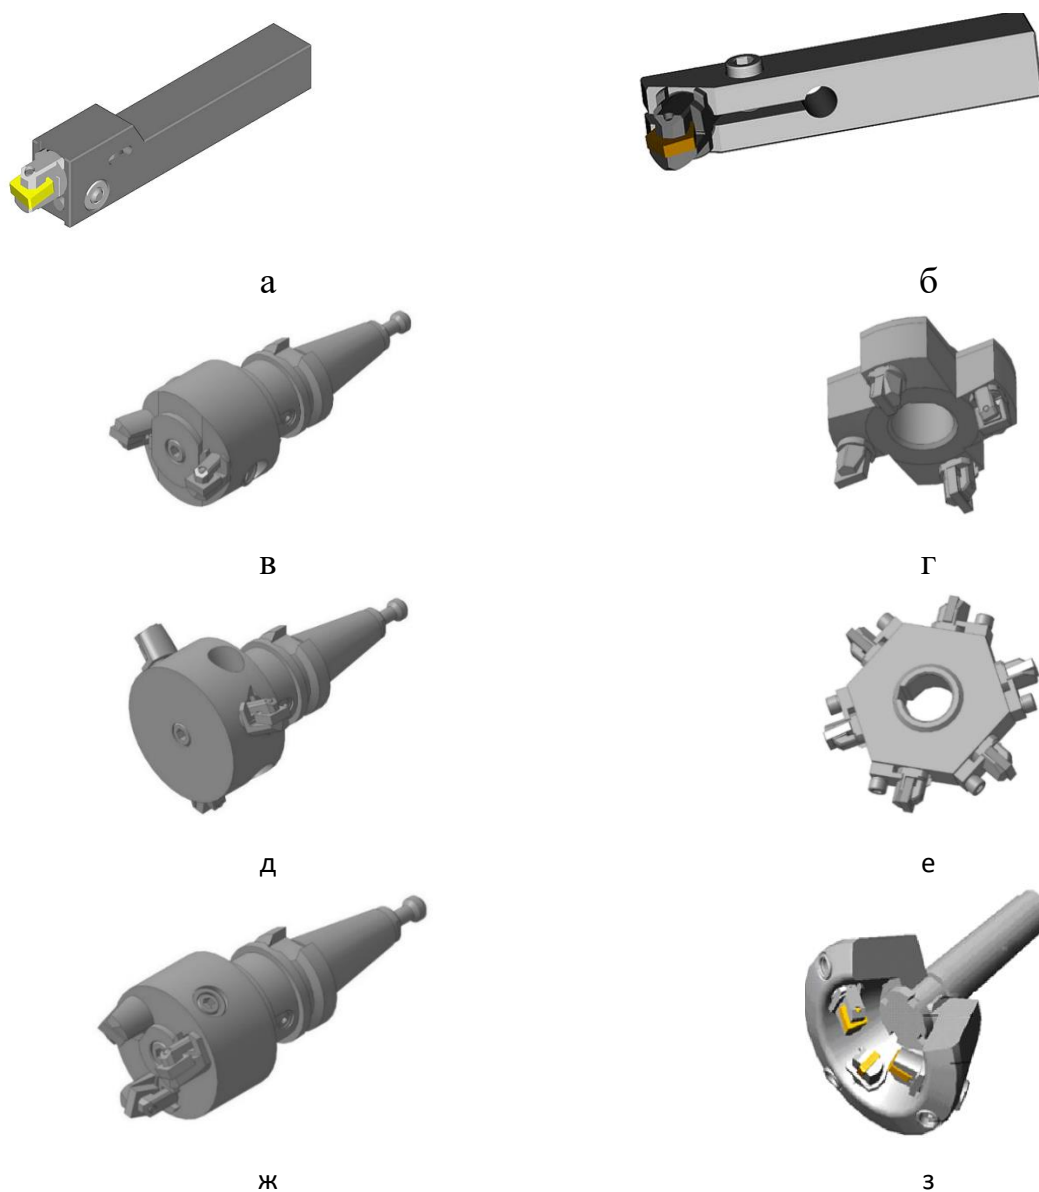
Блочно-модульные режущие инструменты: а – резец проходной; б – резец расточной; в – зенкер концевой; г – зенкер насадной; д – фреза дисковая концевая; е – фреза дисковая насадная; ж – фреза торцовая концевая; з – фреза для охватывающего фрезерования сферических поверхностей деталей
